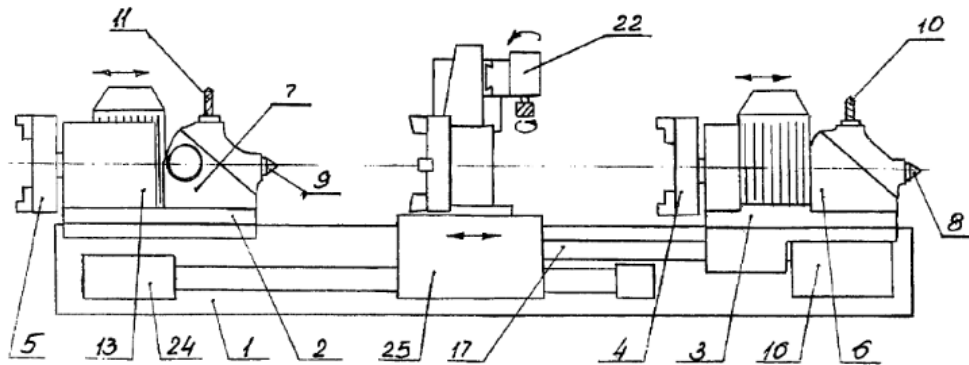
Двухшпиндельный токарный станок по патенту РФ № 56237
